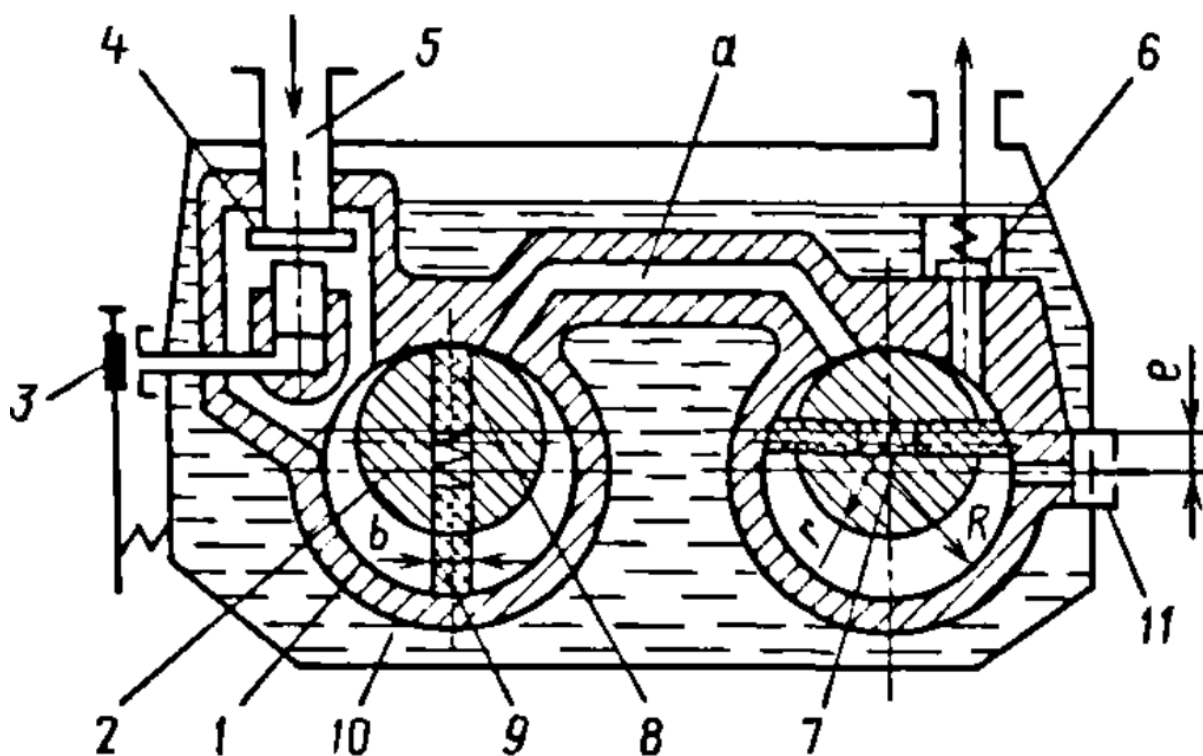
Устройство РВН с масляным уплотнением. 1 – цилиндрический корпус; 2 – эксцентрический ротор первой ступени; 3 – клапан; 4 – сетчатый фильтр; 5 – входной патрубок; 6 – клапан; 7 – пружина; 8, 9 – пластины; 10 – вакуумное масло [4, с. 340]
